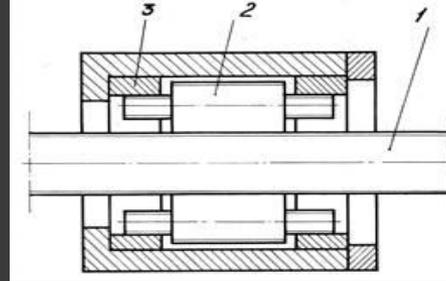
Передача винт – гайка со ступенчатыми резьбовыми роликами
